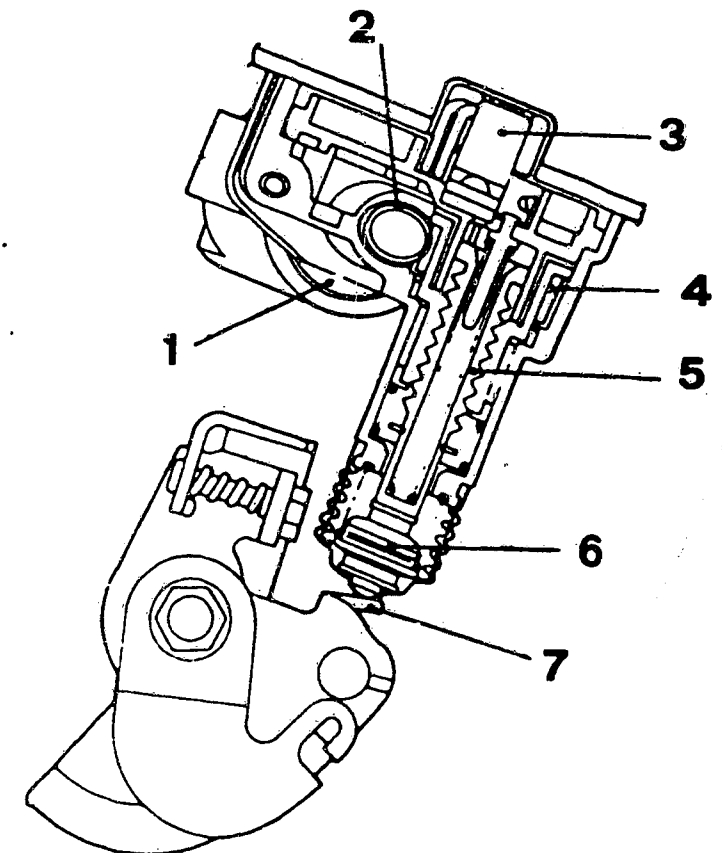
ISC-Schrittmotor im Schnitt: 1 Motor – 2 Schneckengetriebe – 3 Motorpositionssensor MPS – 4 Schneckenrad – 5 Kolben – 6 Leerlaufschalter – 7 ISC-Hebel.
